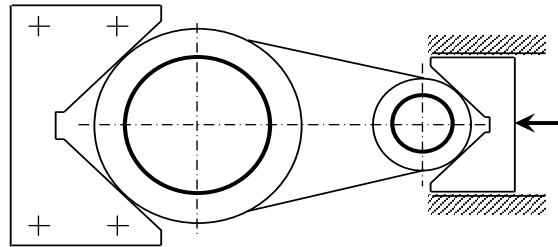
Спрощена конструктивна схема верстатного пристрою
